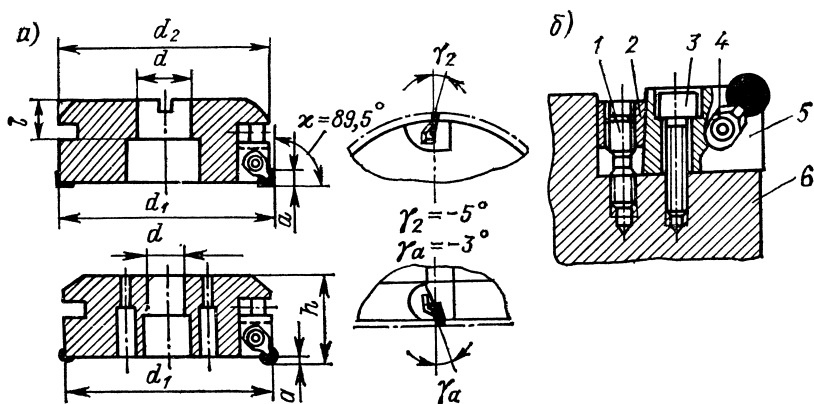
Фреза торцовая насадная, регулируемая фирмы «Планзее» (Австрия): 1 — дифференциальный винт; 2 — клин; 3 — винт; 4 — прихват; 5 — пластина; 6 — корпус
